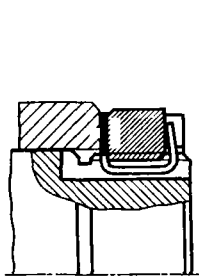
Стопорение кольцевой гайки с торцовыми зубьями шайбой с отгибными лапками
